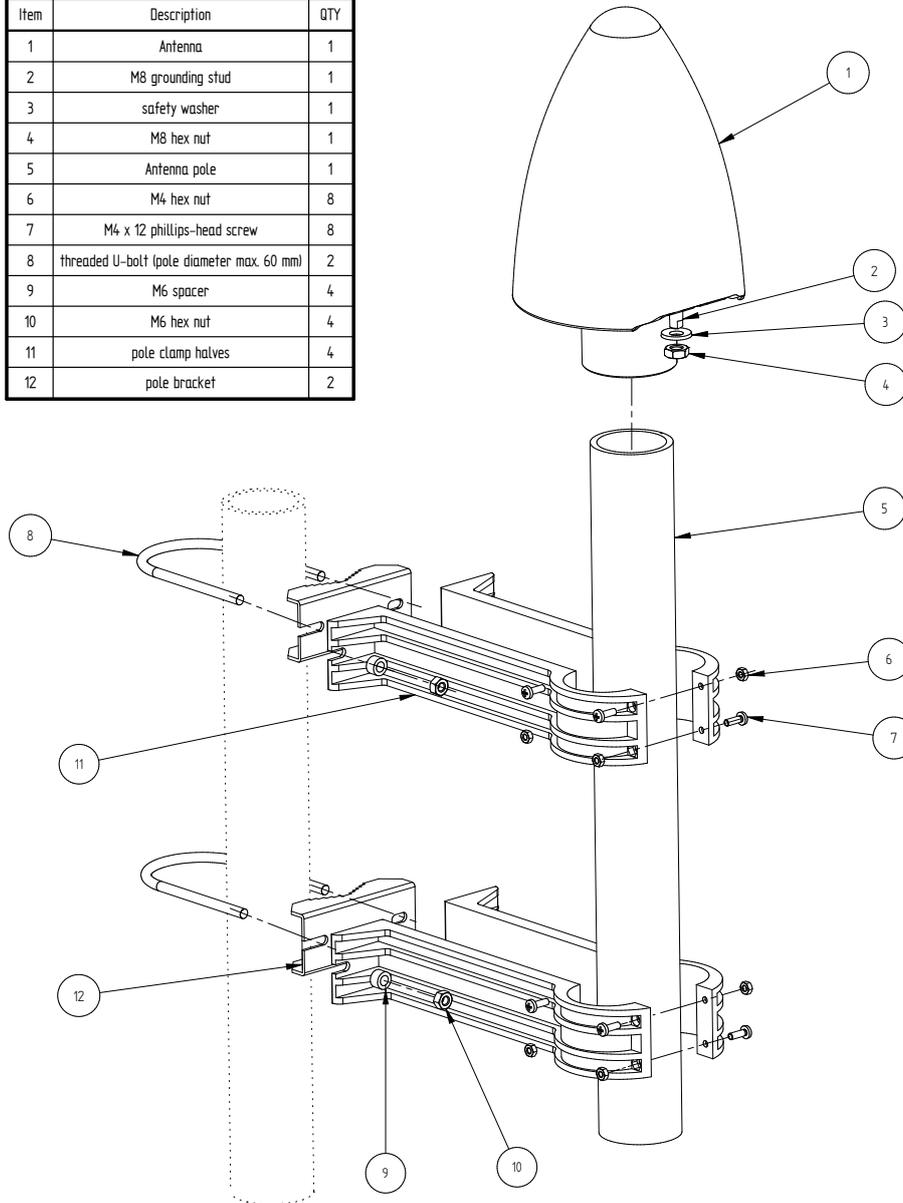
Mastmontage einer Meinberg GPS-Antenne
